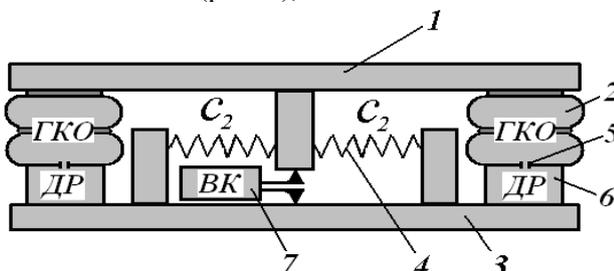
Схема конструкции второй ступени пневматического рессорного подвешивания с применением корректора жесткости и высоторегулирующего клапана: 1 – грузовая платформа, 2 – резинокордная двухгофровая оболочка, 3 – опорная платформа, 4 – пружины корректора жесткости, 5 – дроссельная шайба, 6 – дополнительный резервуар, 7 – клапан высоторегулирующий.
